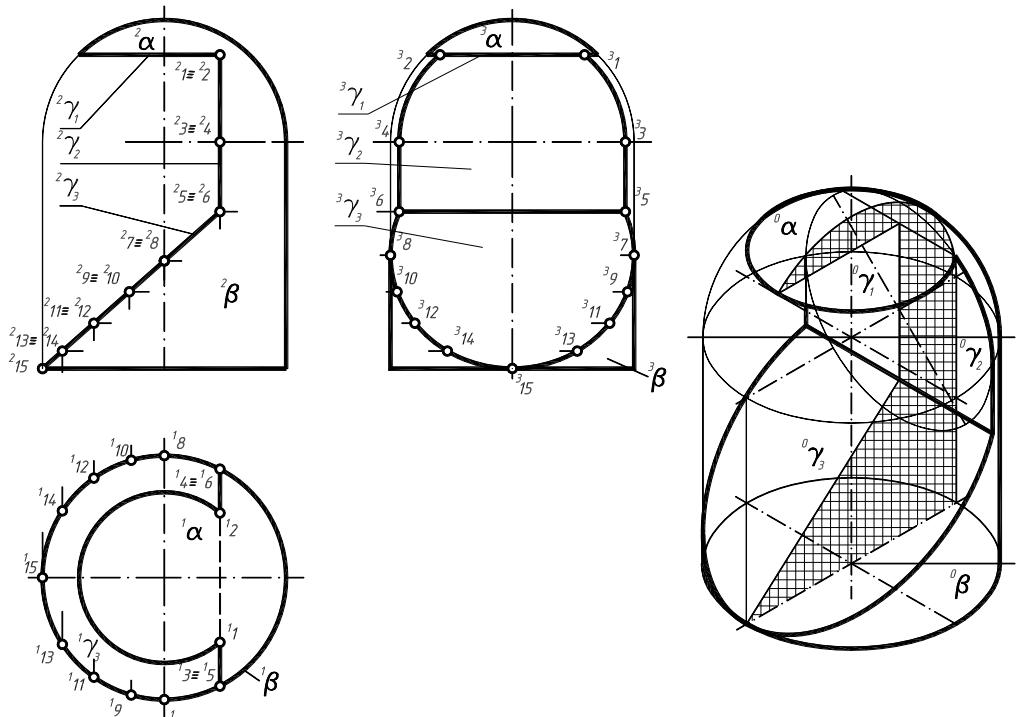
Комплексний кресленик поєднаної сферичної та циліндричної поверхні
